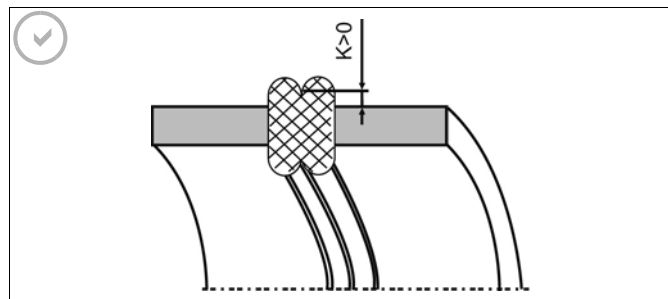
Поперечный разрез правильного стыкового шва
